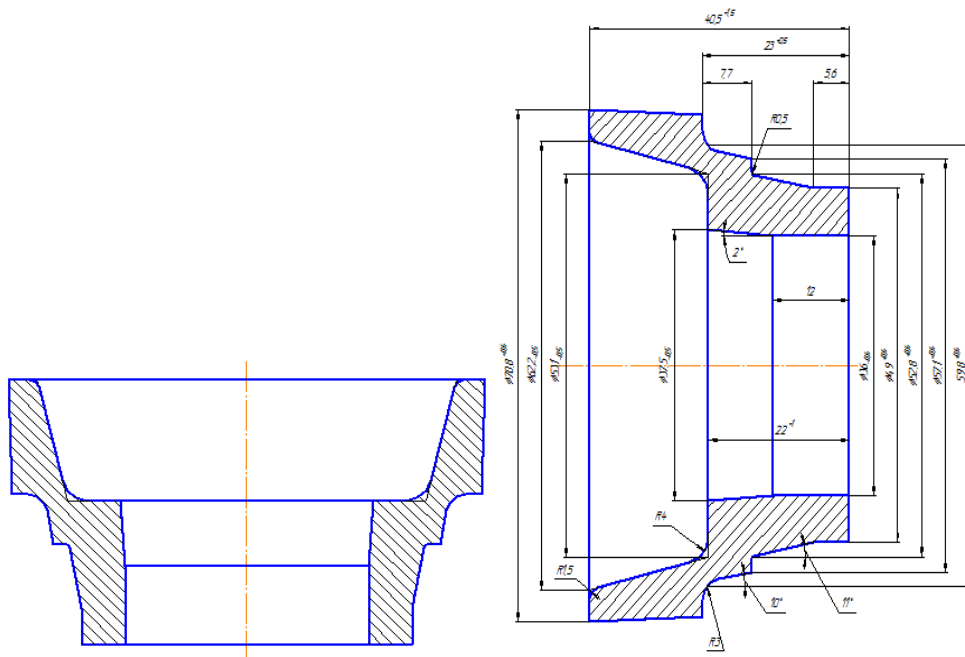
Поковка «башня в ряд» для колец подшипника 2007108
